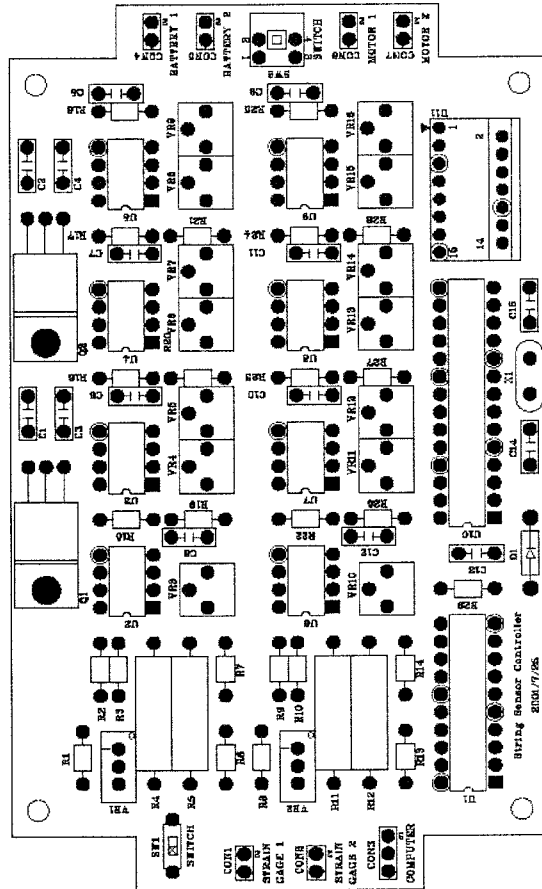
의복형태 조종기 제어기의 PCB 도면
